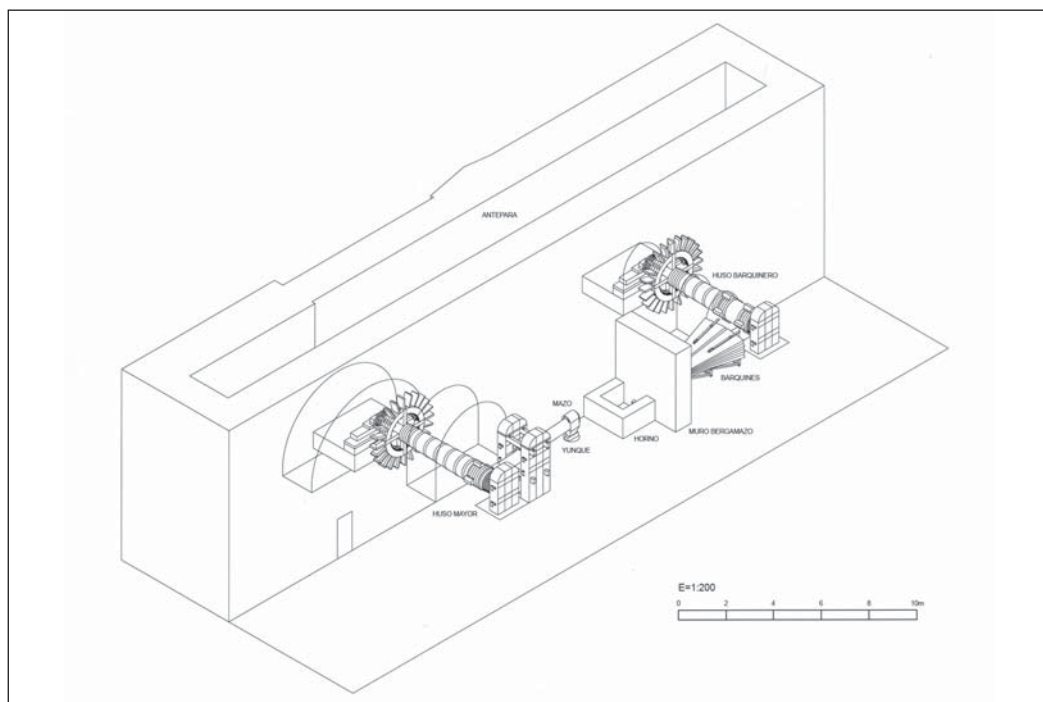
Reconstrucción en 3D de las principales máquinas de las ferrerías hidráulicas. Imagen procedente de Urteaga (2001, p. 248).
